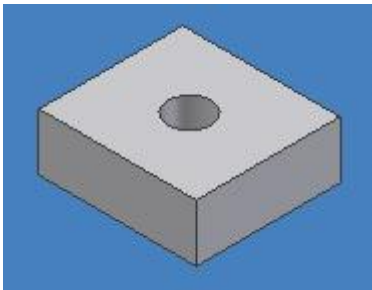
Pieza A8 . Se observa el mecanizado aplicado a 12 piezas según el plano AND00 - 0600
